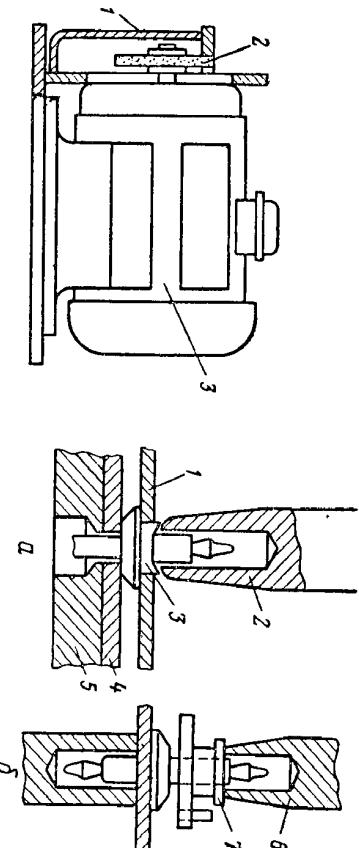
Способы запрессовки оси баланса и двойного ролика:
